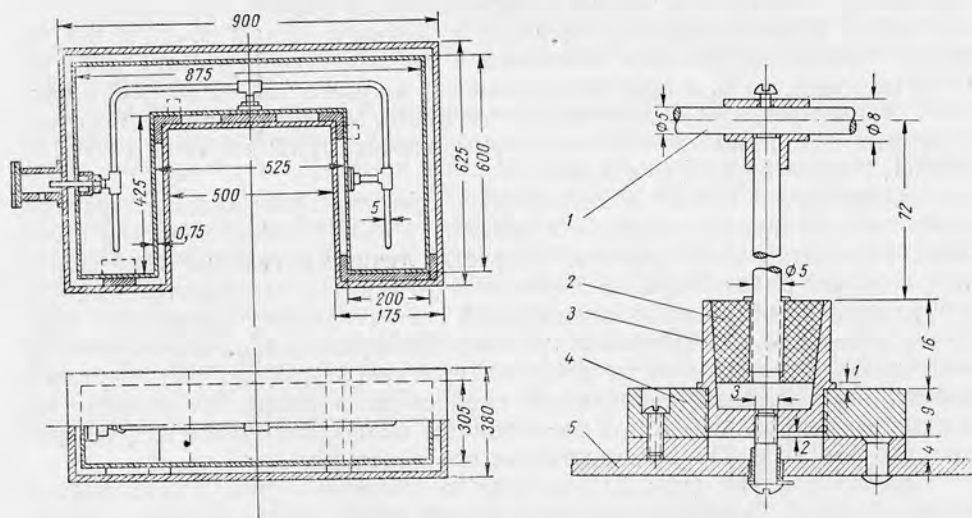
Конструкция камеры и крепления центрального электрода установки РКИ:
